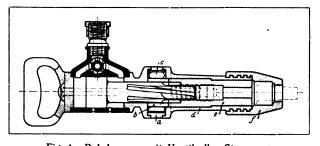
Bohrhammer mit Ventilrollen-Steuerung.
